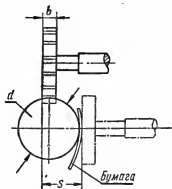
Схема установки фрезы при фрезеровании канавки для сегментной шпонки:
